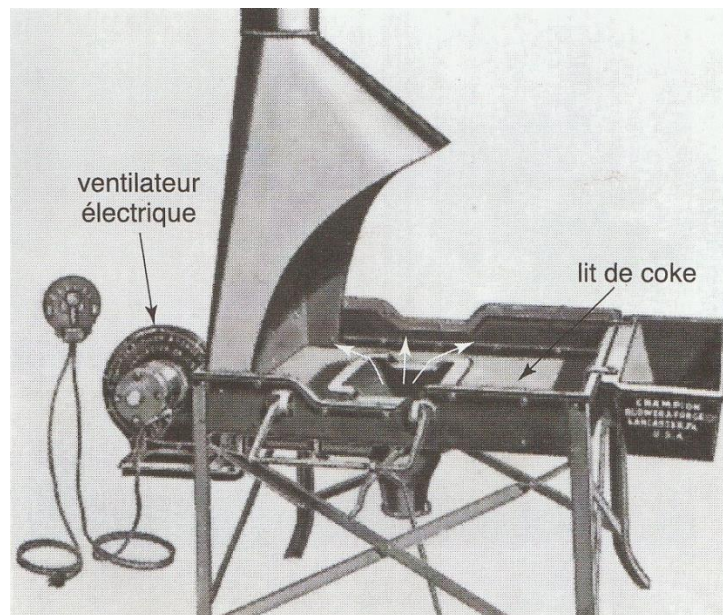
Une forge utilisée pour chauffer le métal pour le soudage par forgeage [13].
